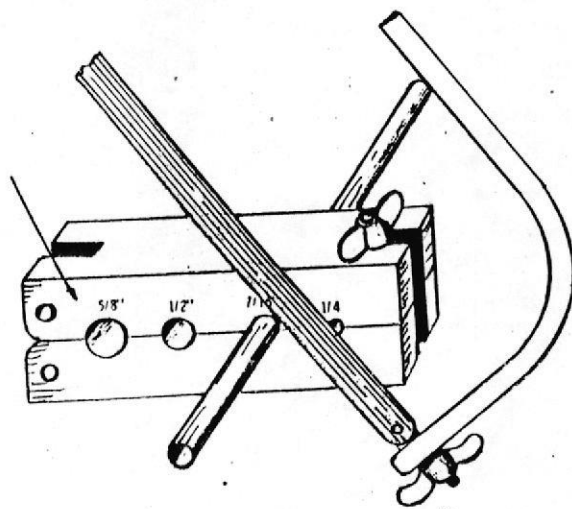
Corte de un tubo con segueta y accesorio de corte.
